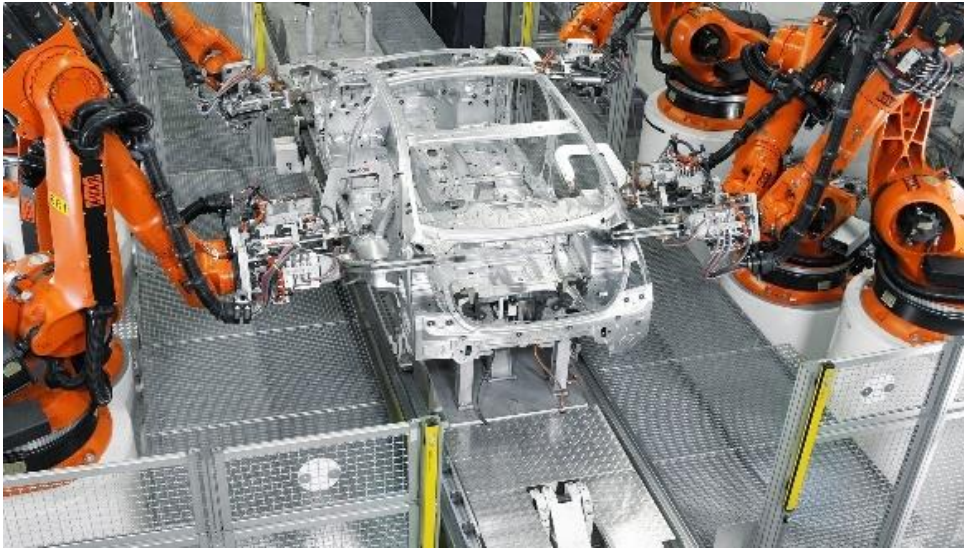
Soldadura por pontos robotizada [41]
